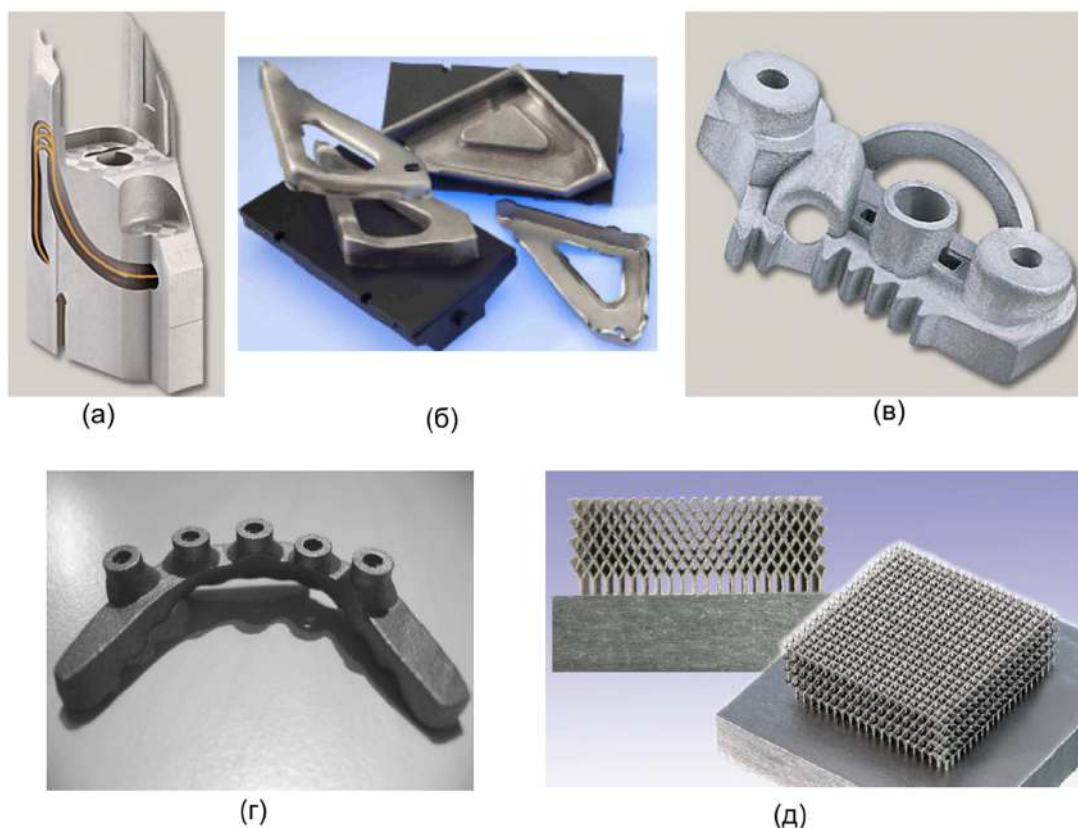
Металлические изделия, изготовленные методами СЛС/СЛП: а – инструментальная вставка литейного штампа из жаропрочной стали с охлаждающими каналами; б – инструмент для гибки листового металла; в – деталь крепежа автомобильного кресла; г – стоматологическая конструкция из сплава Ti-6Al-4V; д – легкая теплообменная структура из нержавеющей стали [157].
